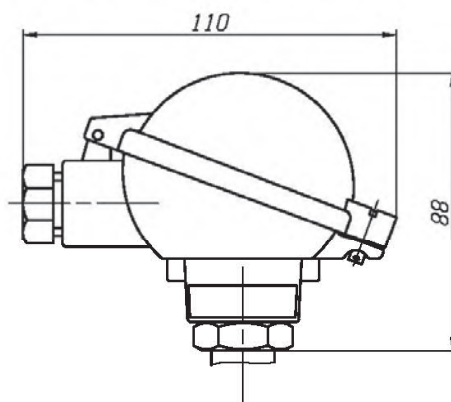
в – Габаритный чертеж ПТ исполнения ТХА 001Сп-Ех1
